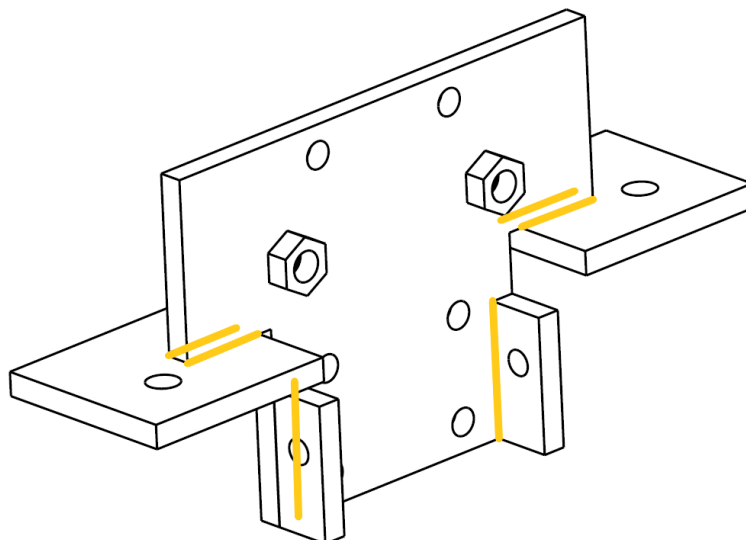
Cordones de soldadura sobre el armazón definitivo.
